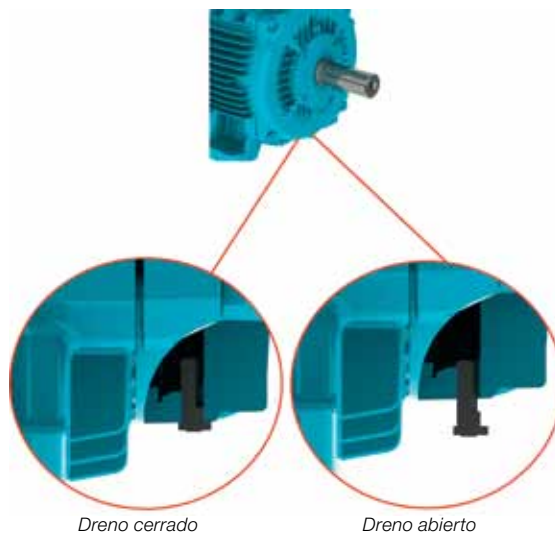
Detalle del drenaje en la tapa delantera (160-355)
